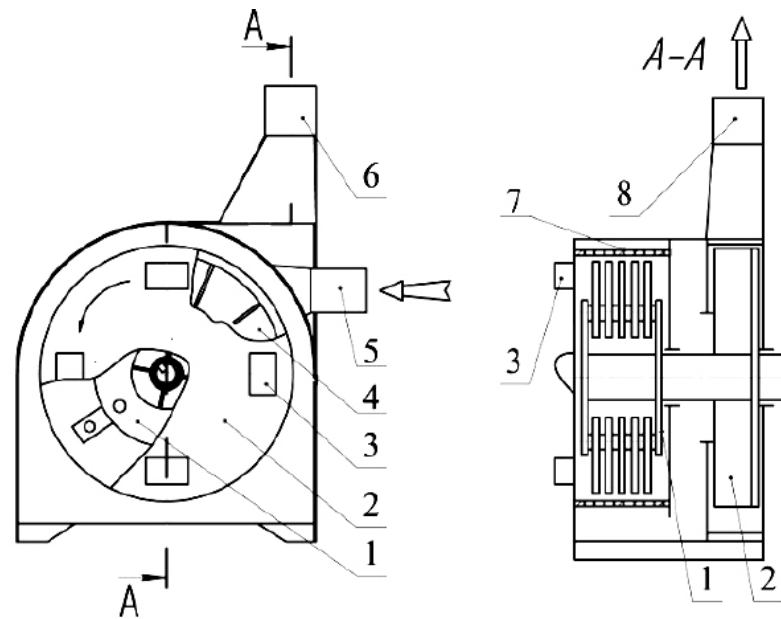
Дробилка с жалюзийными сепараторами: 1-ротор; 2 и 3-молотки; 4-камера; 5-кольца рифленые; 6-внешняя камера; 7-кольцо; 8-сепарирующие жалюзийные элементы; 9-загрузочная горловина; 10-осадитель
